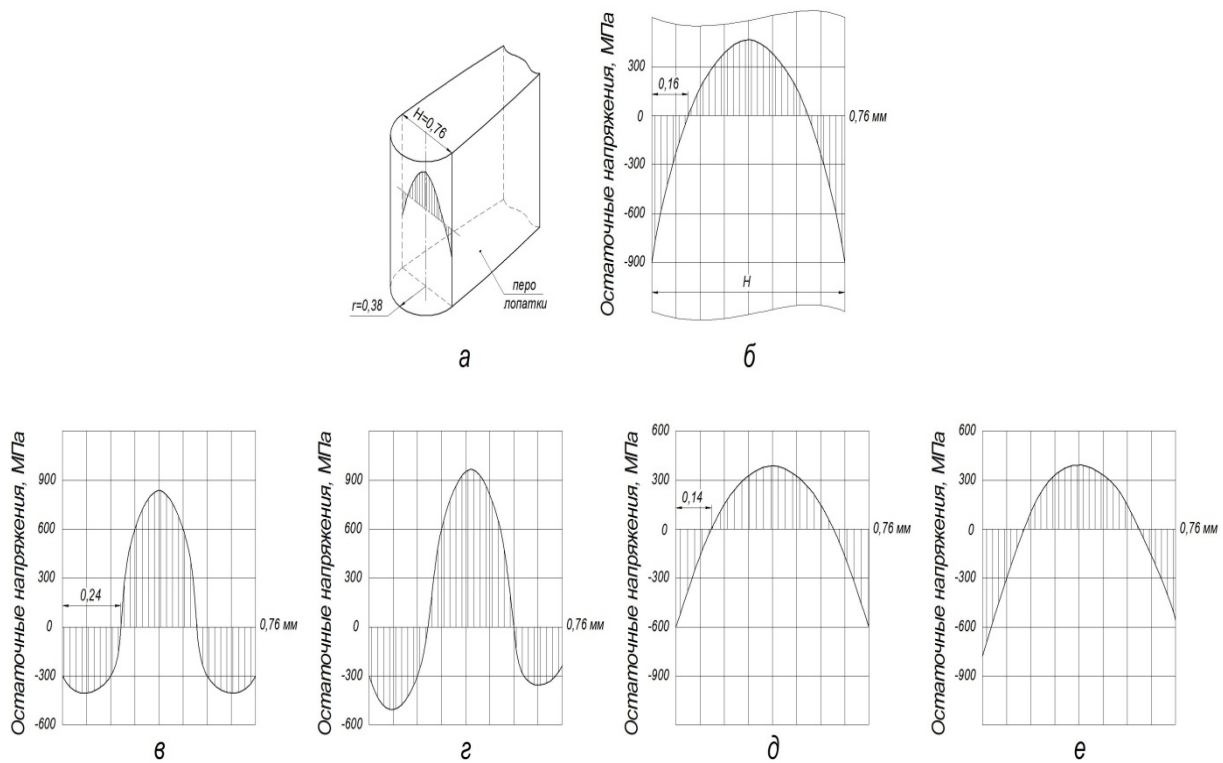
Напряжения в перо рабочей лопатки третьей ступени компрессора низкого давления:
